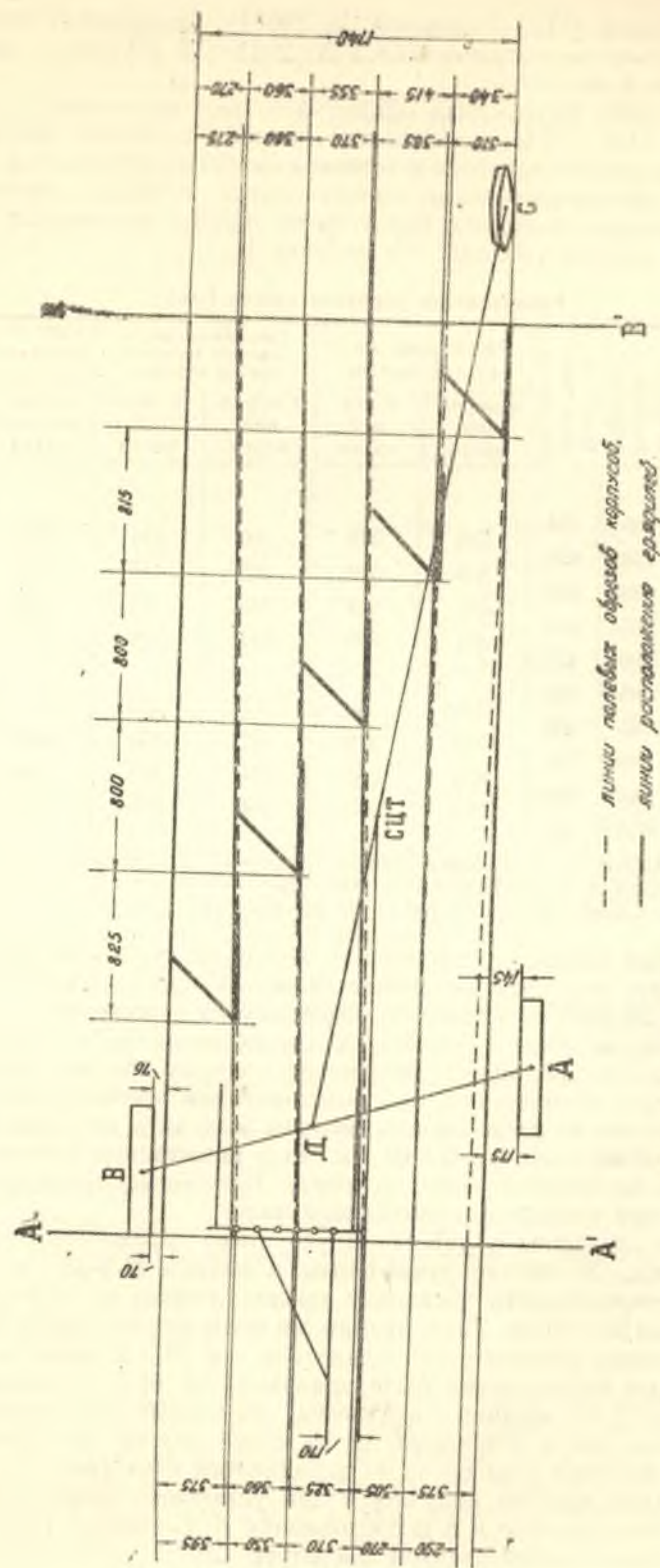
Расположение корпусов, колес и грядки плуга П-5-35М.
